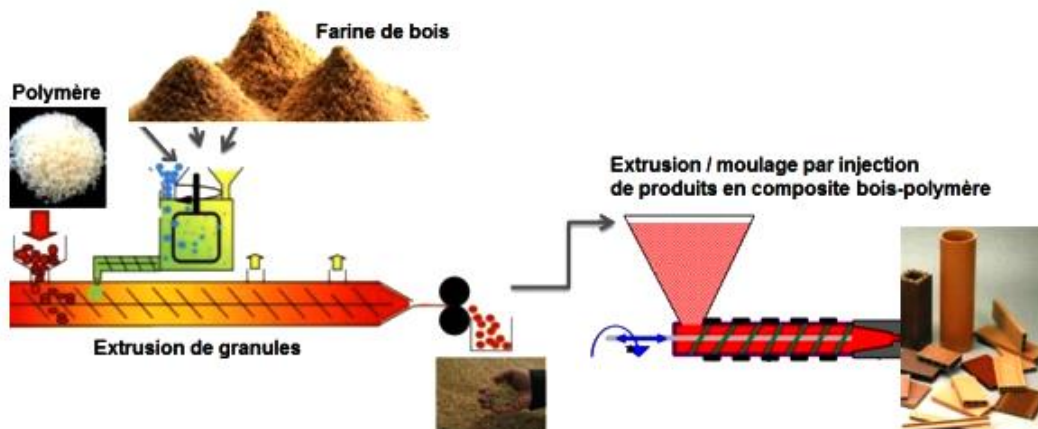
11. Procédé de moulage par injection des SNFT [37].
